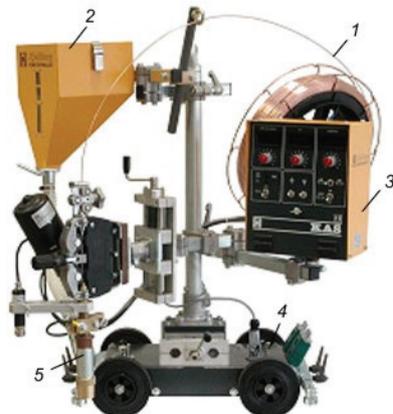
Общий вид сварочного автомата для автоматической сварки под флюсом:
